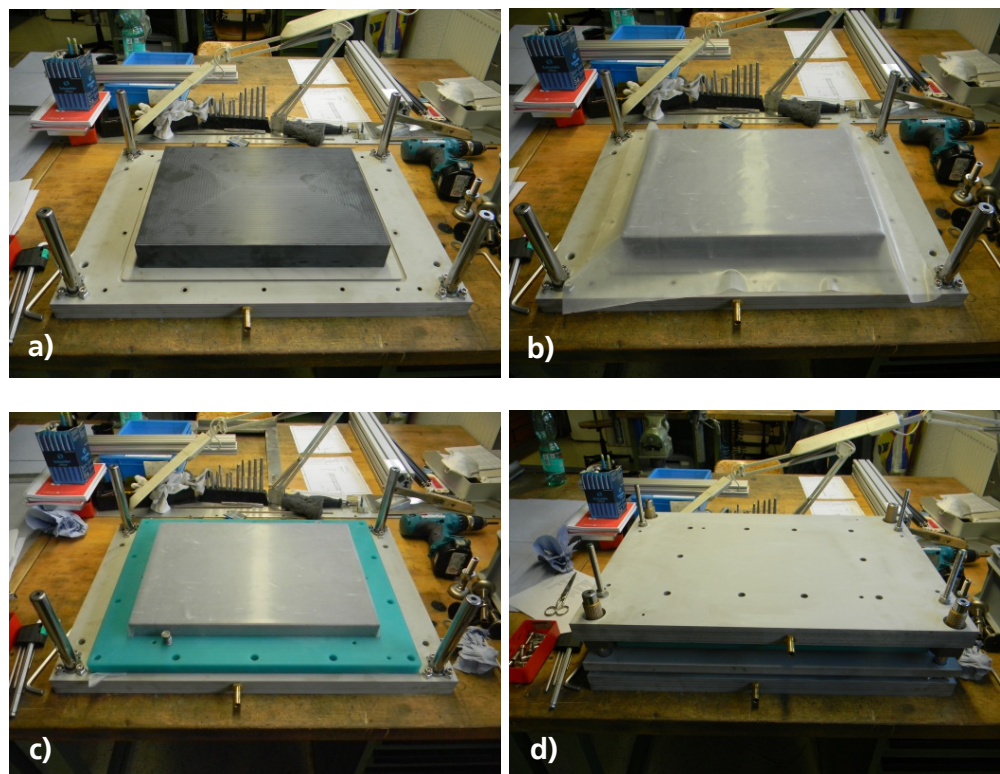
Werkzeug für das Membran-Vakuumtiefziehverfahren: a) späteres Oberteil mit Formplatte (noch ohne Kanäle), b) Silikonmembran aufgelegt, c) Silikonmembran geklemmt und gespannt, d) Werkzeug zusammengebaut (später umgedreht)
